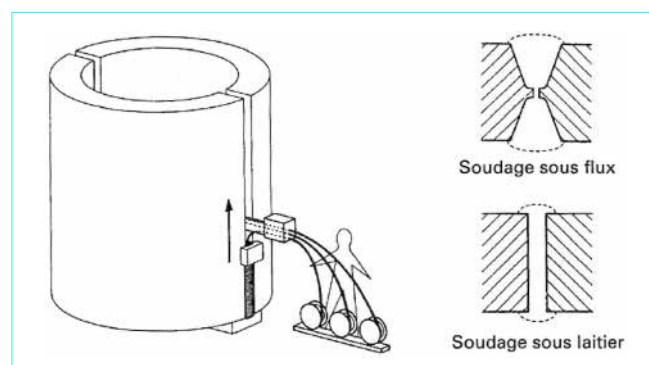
Soudage vertical sous laitier : application sur une virole
